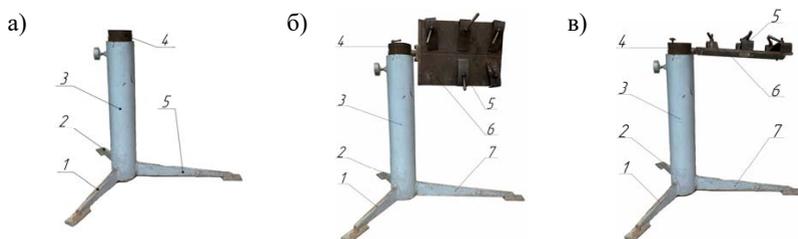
Лабораторные стойки для сварки плавлением:
